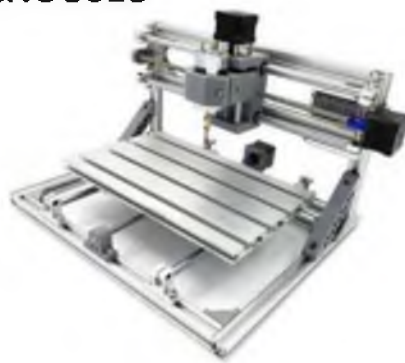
Фрезерно-гравировальная установка CNC 3018 [2]
